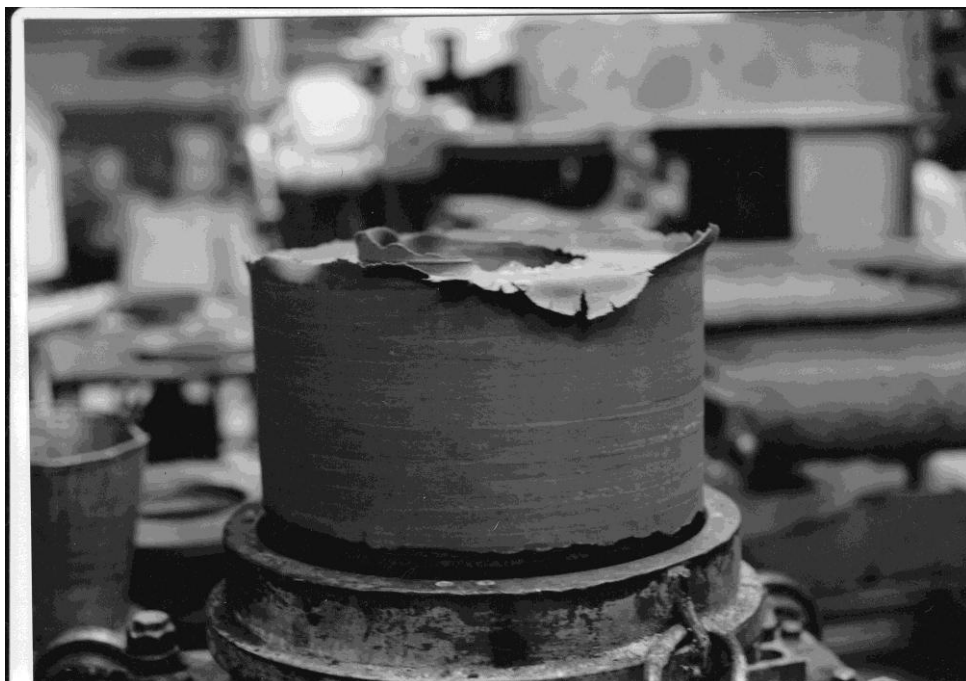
Прессованная заготовка после извлечения из пресс-формы
